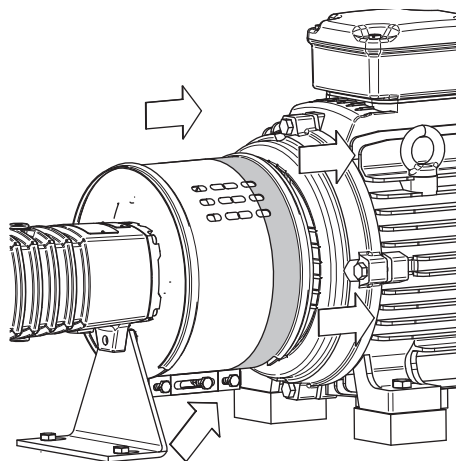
Einstellen des Mantels auf der Motorseite.
